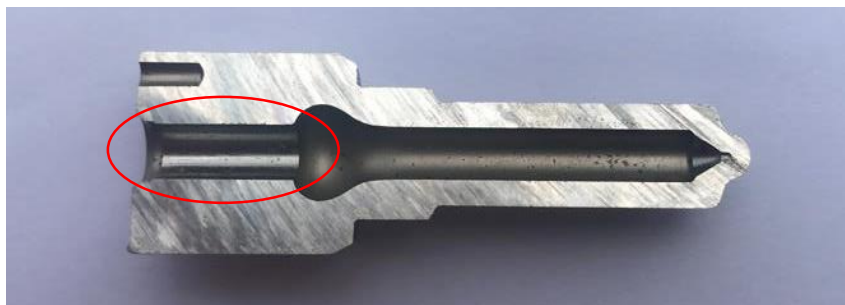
Corte transversal do bico injetor de combustível com destaque para o diâmetro de guia
